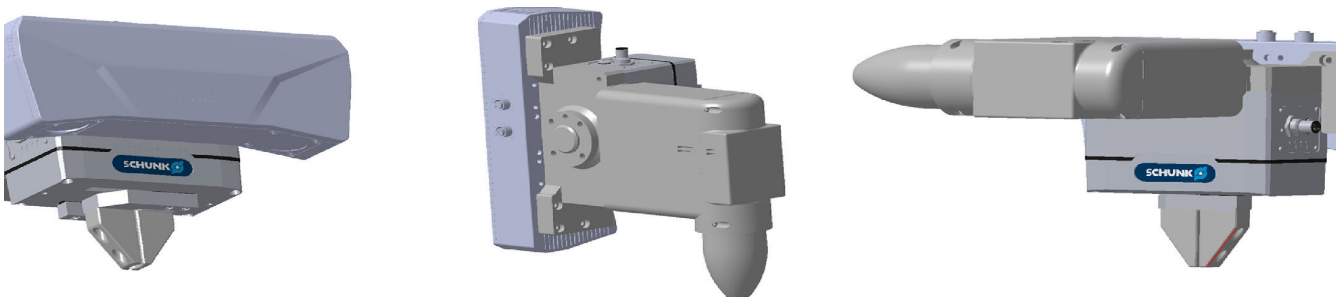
Flexibles Werkzeug bestehend aus 3D-Kamera (links), Schrauber (Mitte) und Greifer (rechts). Grafik: Fraunhofer IWU
